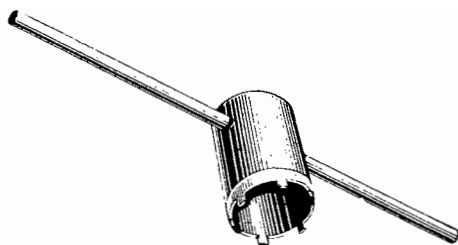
Ключ 48001-1-027МД для гайки оси поддерживающего катка КВ-34-11
